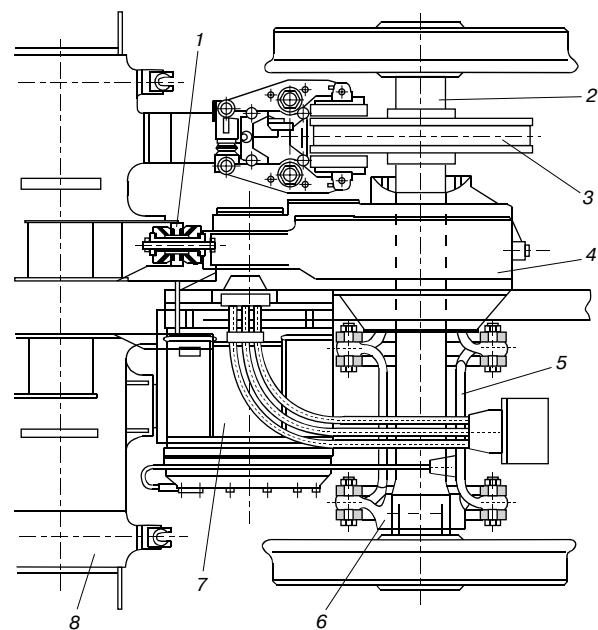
Одноосная тележка и моторно-редукторный блок:
